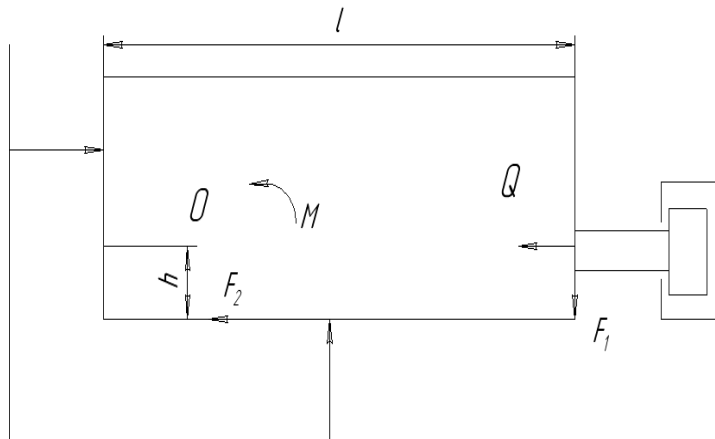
Схема для розрахунку зусилля затискача коробки передач
